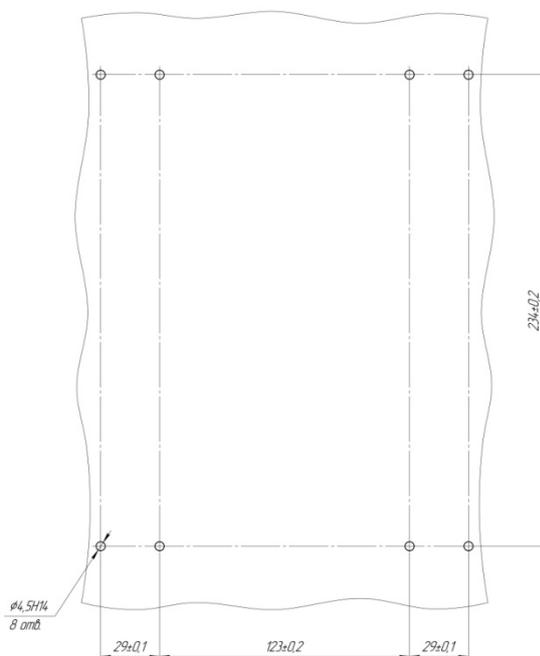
Габаритные и присоединительные размеры устройства РС83-ВС при внешнем монтаже, обеспечивающем его поворот вверх/вниз
